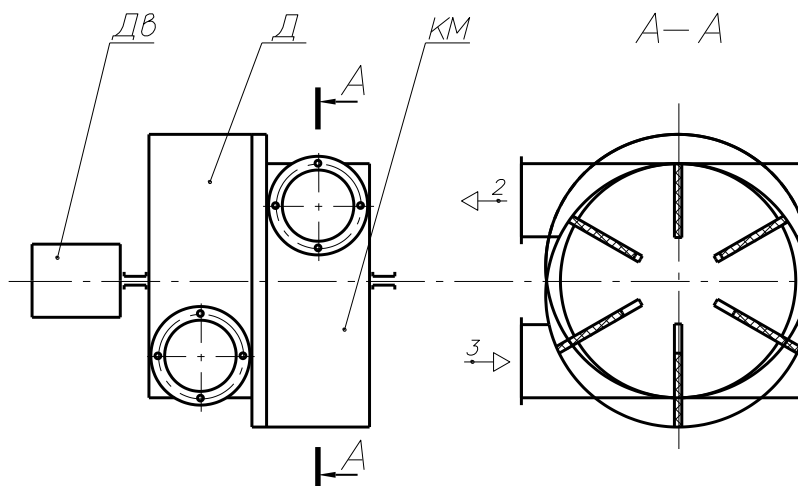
Компресорно-детандерний агрегат роздільного розміщення робочих порожнин:
